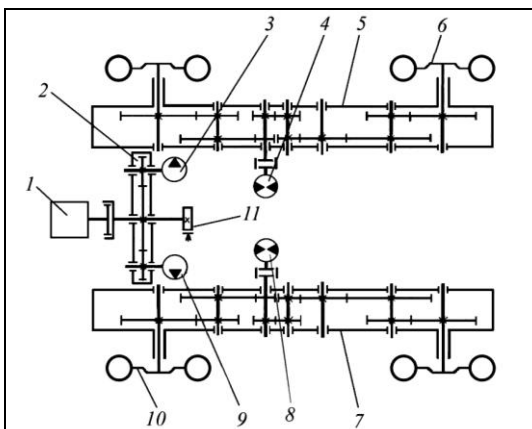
Кинематическая схема колесного погрузчика с бортовым поворотом:
